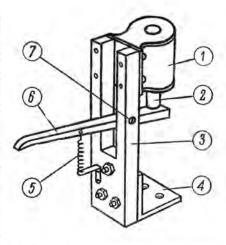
Электромагнитный механизм подошвы ноги: 1— катушка электромагнита; 3— серденик электромагнита; 3— стойка; 4— угловой дюралюминий (25×25 мм); 5 пружина; 6— собачка; 7— ось собачки.
